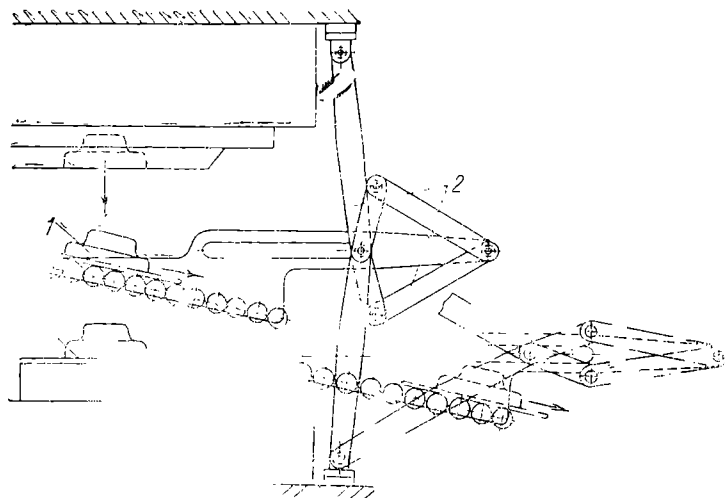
Шарнирно-рычажный сбрасыватель отштампованных деталей и отходов:
